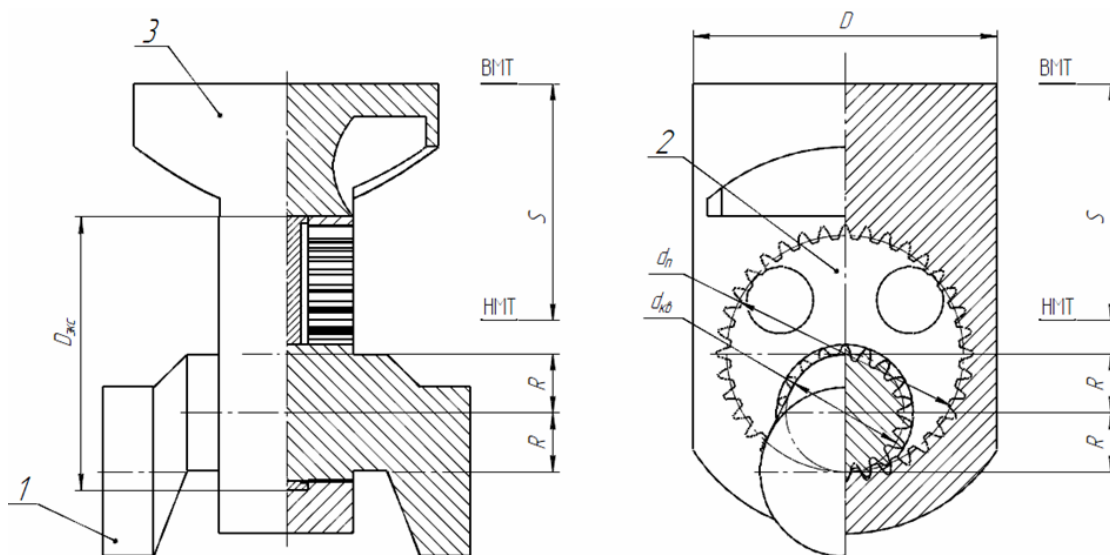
Конструкция бесшатунного механизма: 1 – коленчатый вал (КВ);
